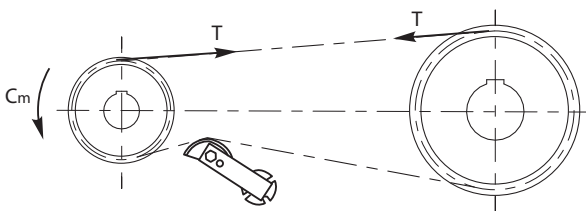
MONTAGGIO CORRETTO - SCONSIGLIATO
